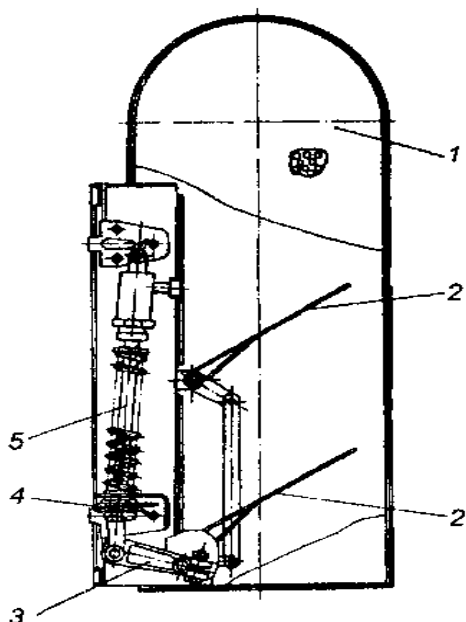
Воздухозаборник блока радиаторов дизеля: 1 – воздухозаборник; 2 – клапан; 3 – рычаг; 4 – шплинт; 5 – шток гидроцилиндра
